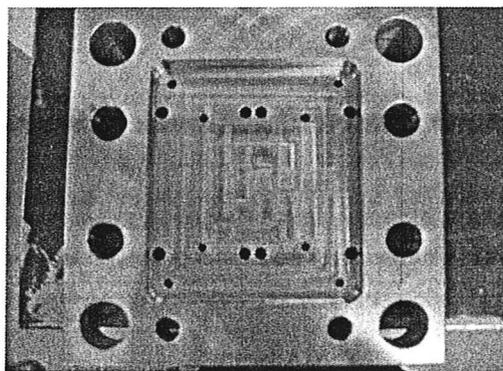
แสดงแผ่นปลด Runner (Fixed Installation Plate)
